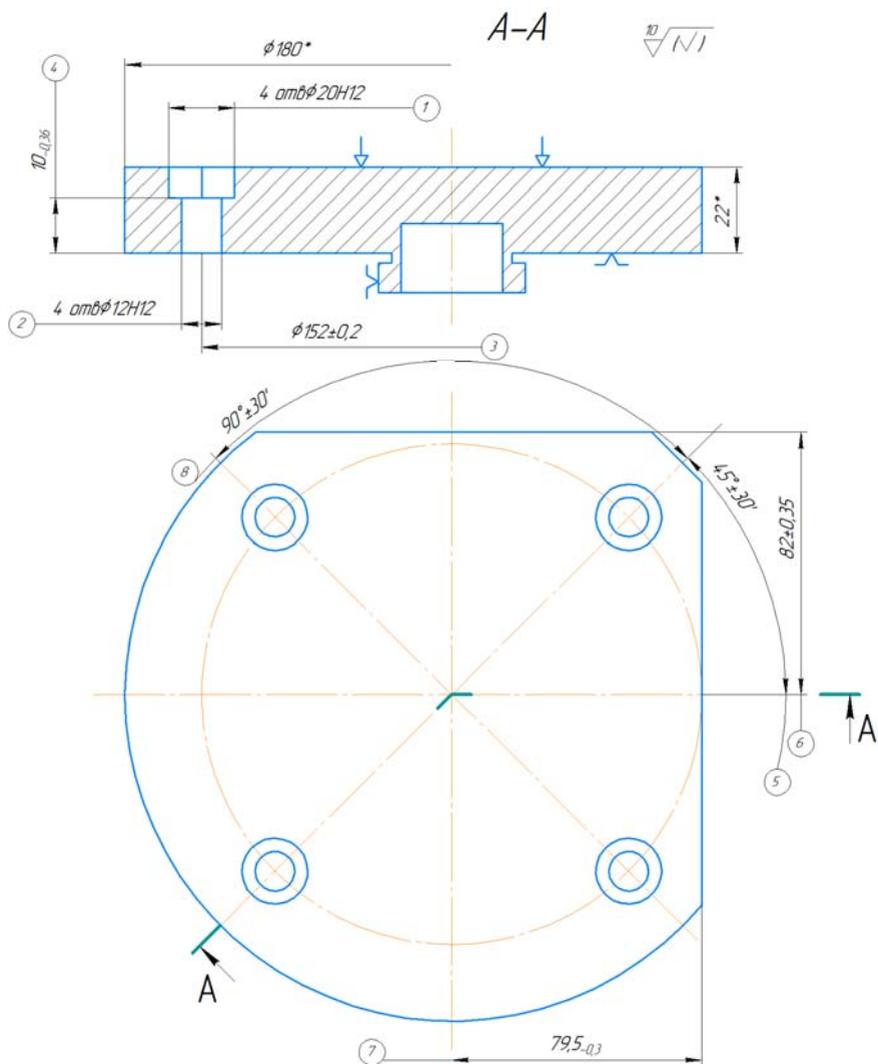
Эскизы заготовки из серого чугуна СЧ20 и комплексной операции обработки детали «Фланец» на станке модели 2254ВМФ4
